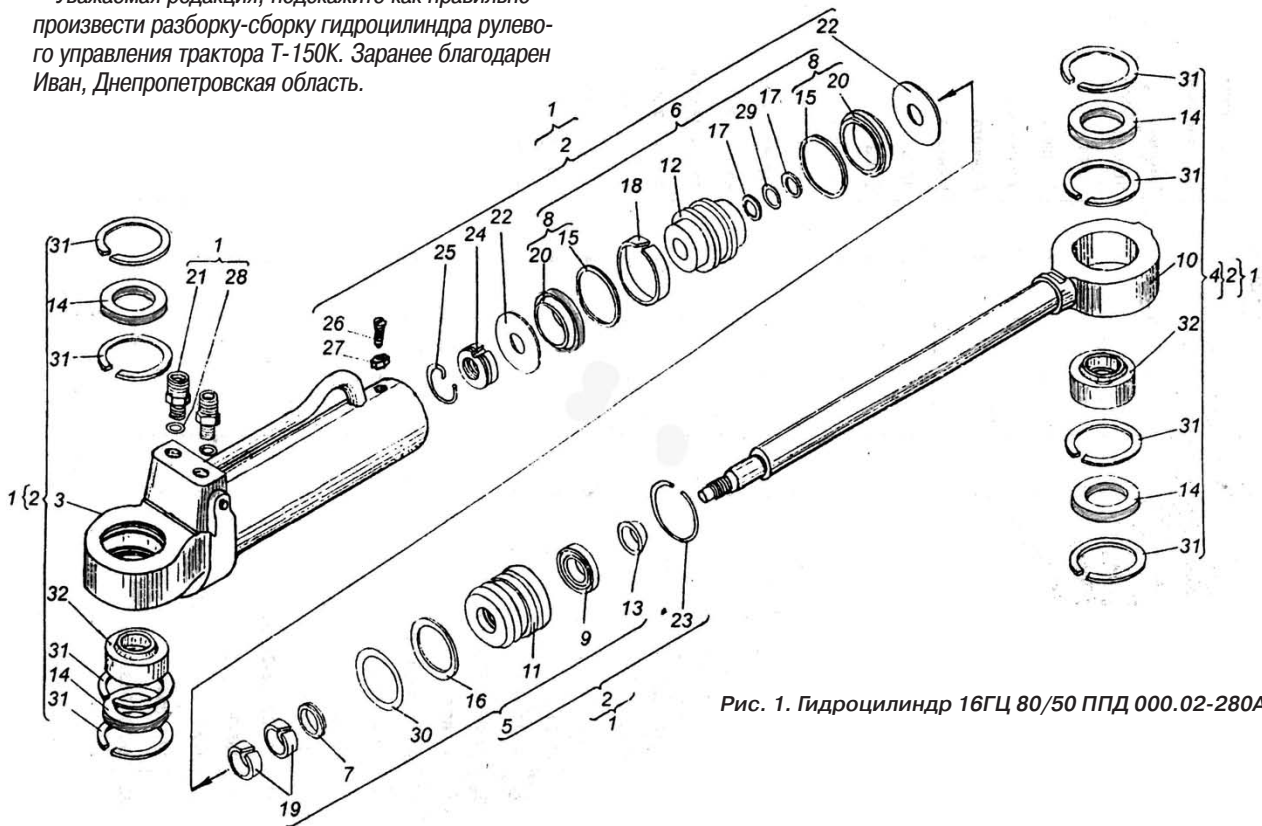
Гидроцилиндр 16ГЦ 80/50 ППД 000.02-280А
